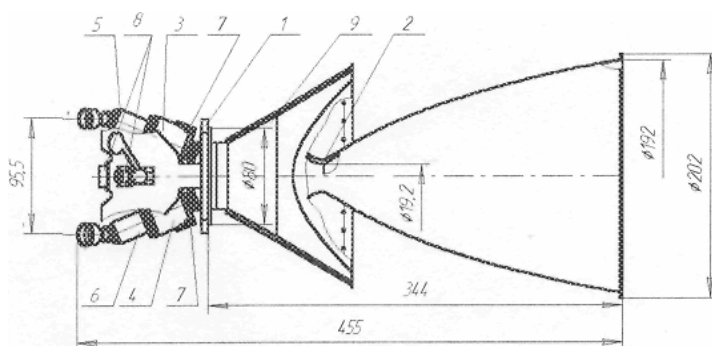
Двигатель РДМТ400А. 1 - смесительная головка; 2 - камера сгорания с соплом; 3 - клапан горючего; 4 - клапан окислителя; 5 - стабилизатор расхода горючего; 6 - стабилизатор расхода окислителя; 7 - электронагреватели; 8 - электрические кабели с соединениями; 9 - теплоизоляционный экран камеры сгорания
